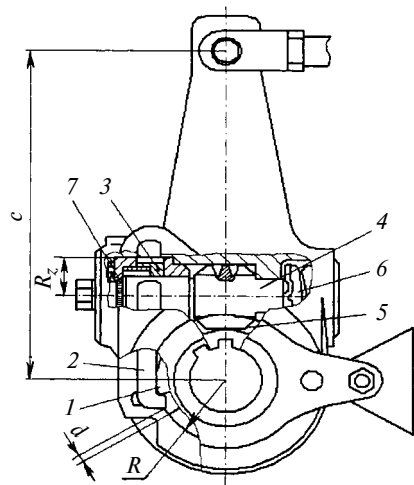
Автоматический регулировочный рычаг Haldex AA1:
